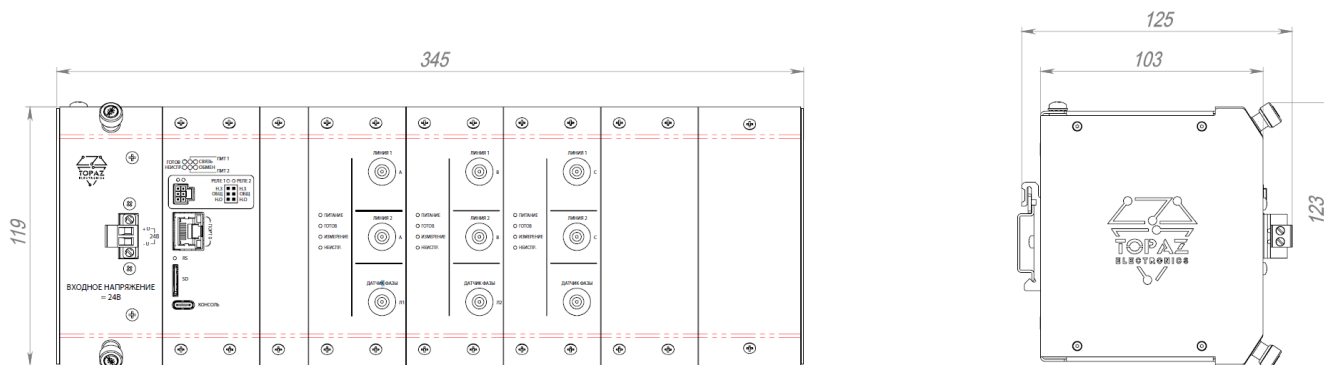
Общий вид и габаритные размеры измерителя ЧР
